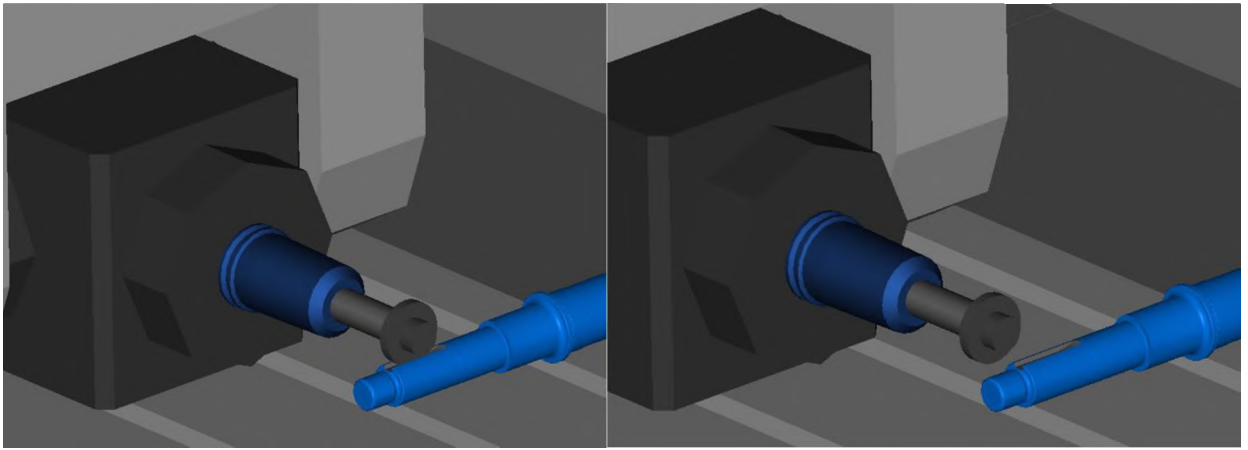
Фрезерування шпонкового пазу дисковою фрезою
